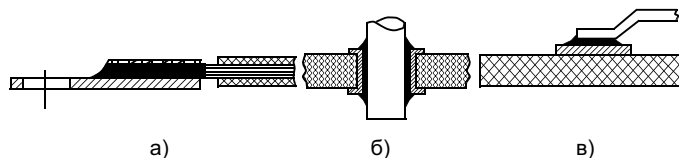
Схемы конструкции электромонтажных соединений: а — соединение провода с клеммой; б, в — штырьковый и планарный выводы ЭРЭ соответственно
